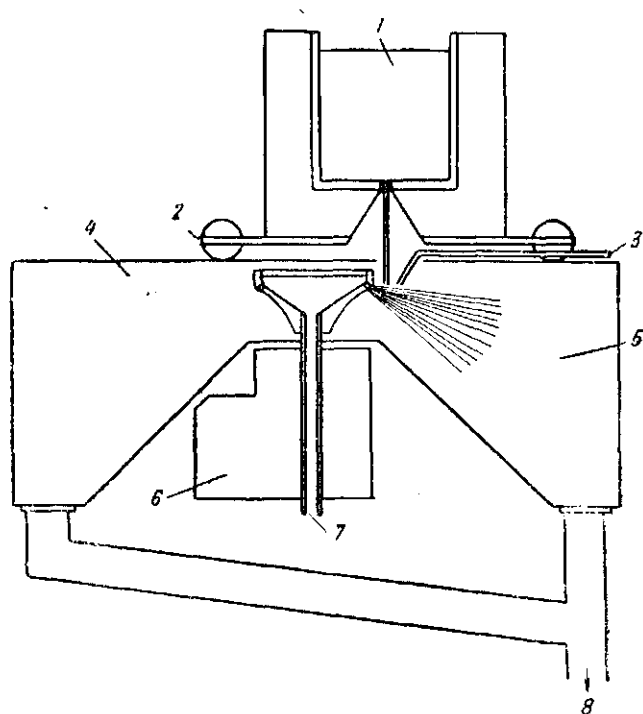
Установка для центробежного распыления расплавов (Гробе и Робертс):
